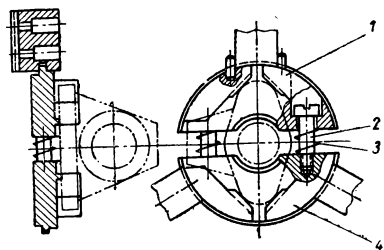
Дополнительные кулачки для зажима деталей больших размеров.
